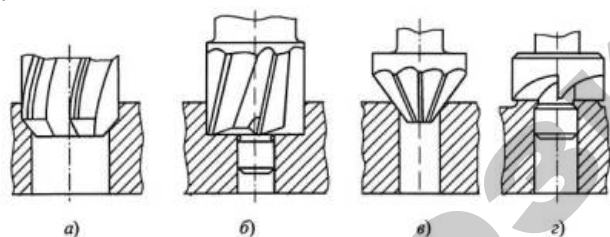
Типы зенкеров: цилиндрический зенкер (а); зенковки (б, в, г)
